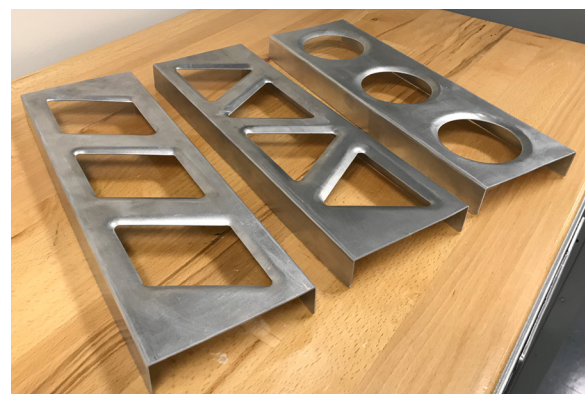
Beispiele für Formteile mit den in Abbildung 2-4 gezeigten Stanzwerkzeugen
